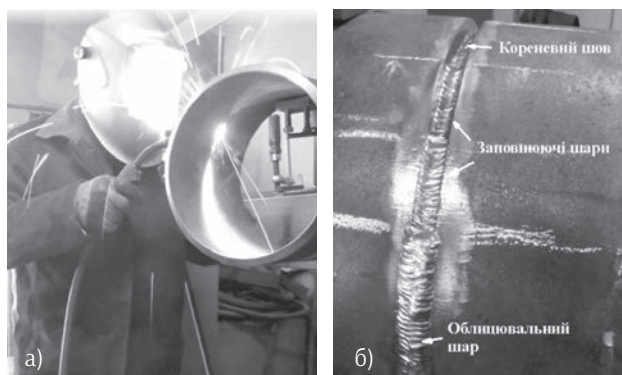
Механизированная сварка неповоротного кольцевого стыкового соединения: а) процесс сварки корневого шва; б) общий вид кольцевого шва с раскладкой по отдельным слоям
